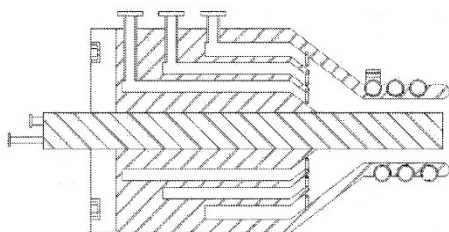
Головка для формування тришарової трубчастої заготовки (пат. № CN214726299U)
